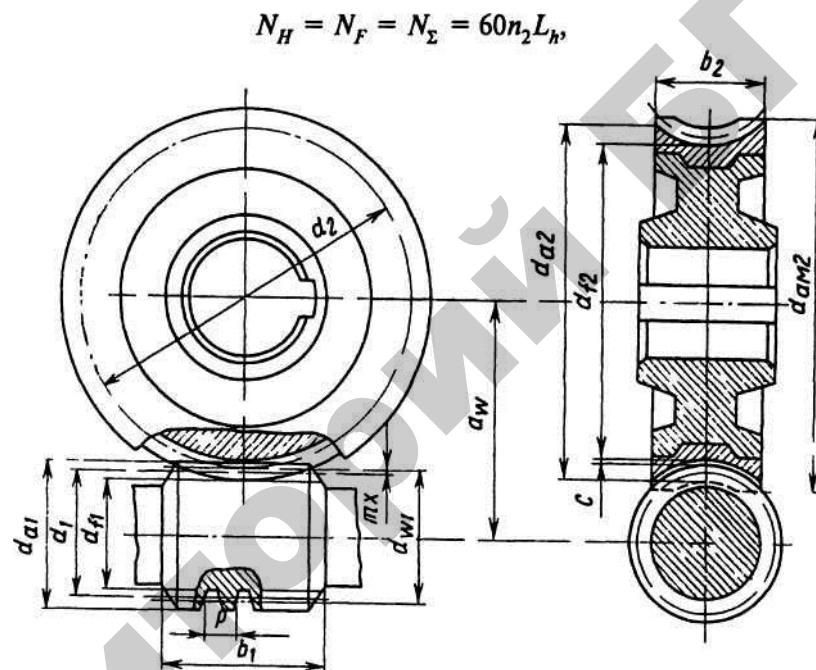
Компонировочный чертеж червячной передачи
